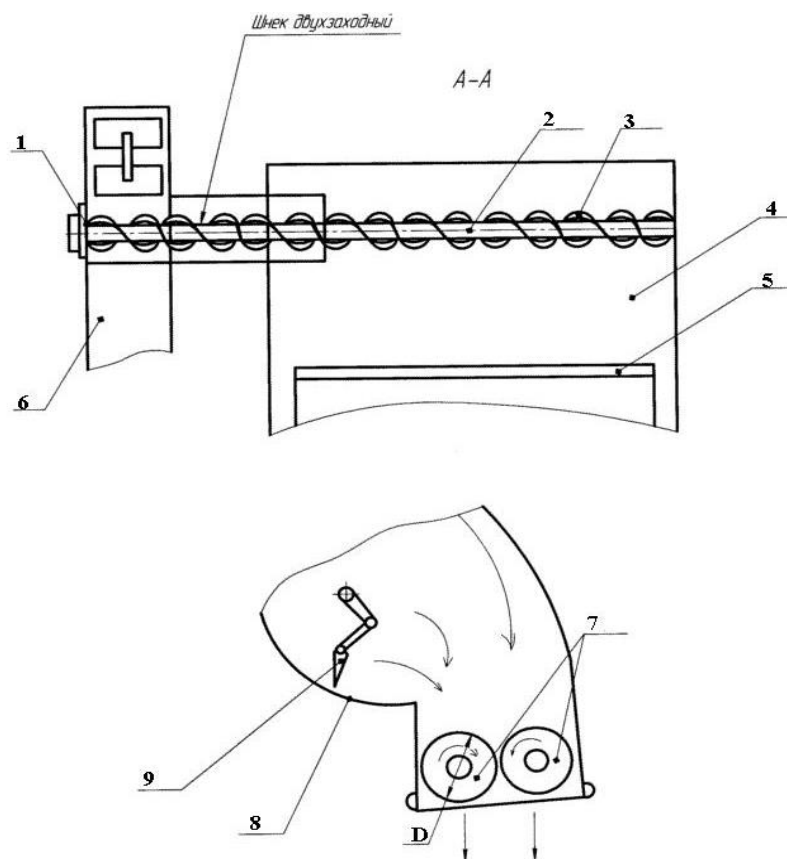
; Рис.5 Комбайн зерноуборочный гусеничный
